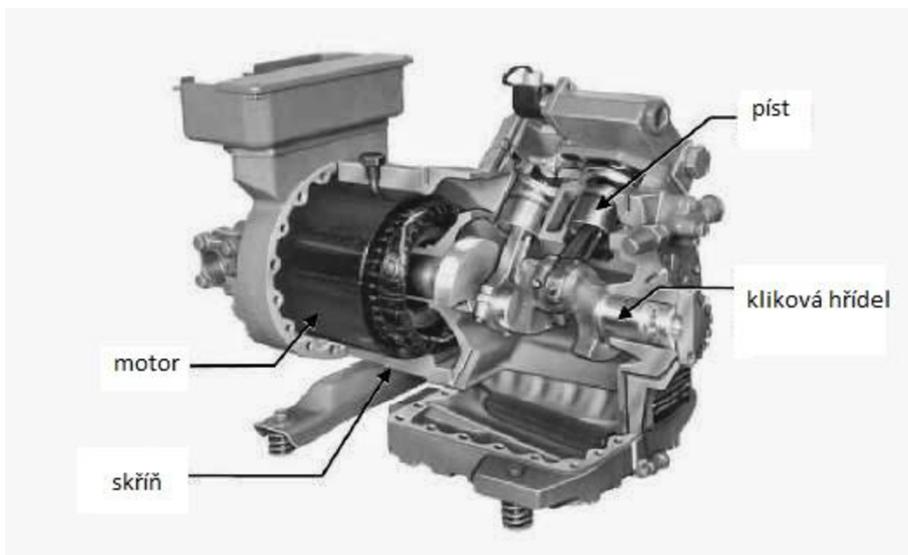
Jednotlivé díly hermetického kompresoru [6]
